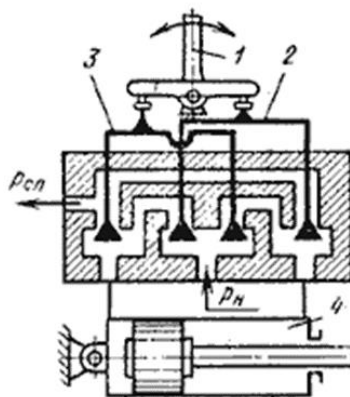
Клапанный гидрораспределитель четырехлинейный с качающимся рычагом управления
